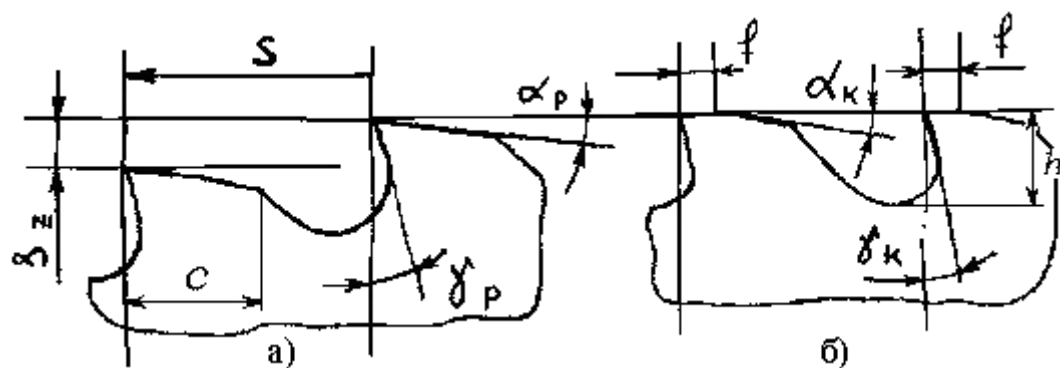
Профиль: а) режущих и б) калибрующих зубьев протяжки.
